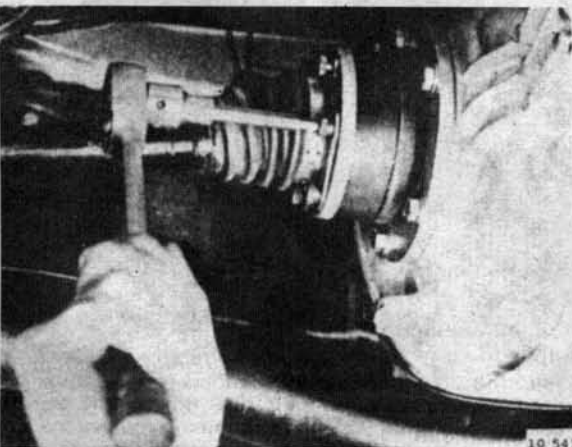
Отсоединение приводных полуосей в автомобилях с двигателями В19 и В200
